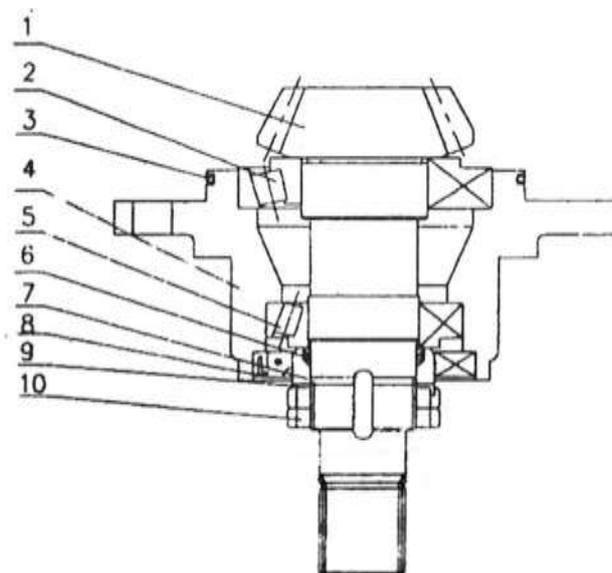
Предварительная затяжка подшипника приводной конической шестерни, в передней центральной передаче
